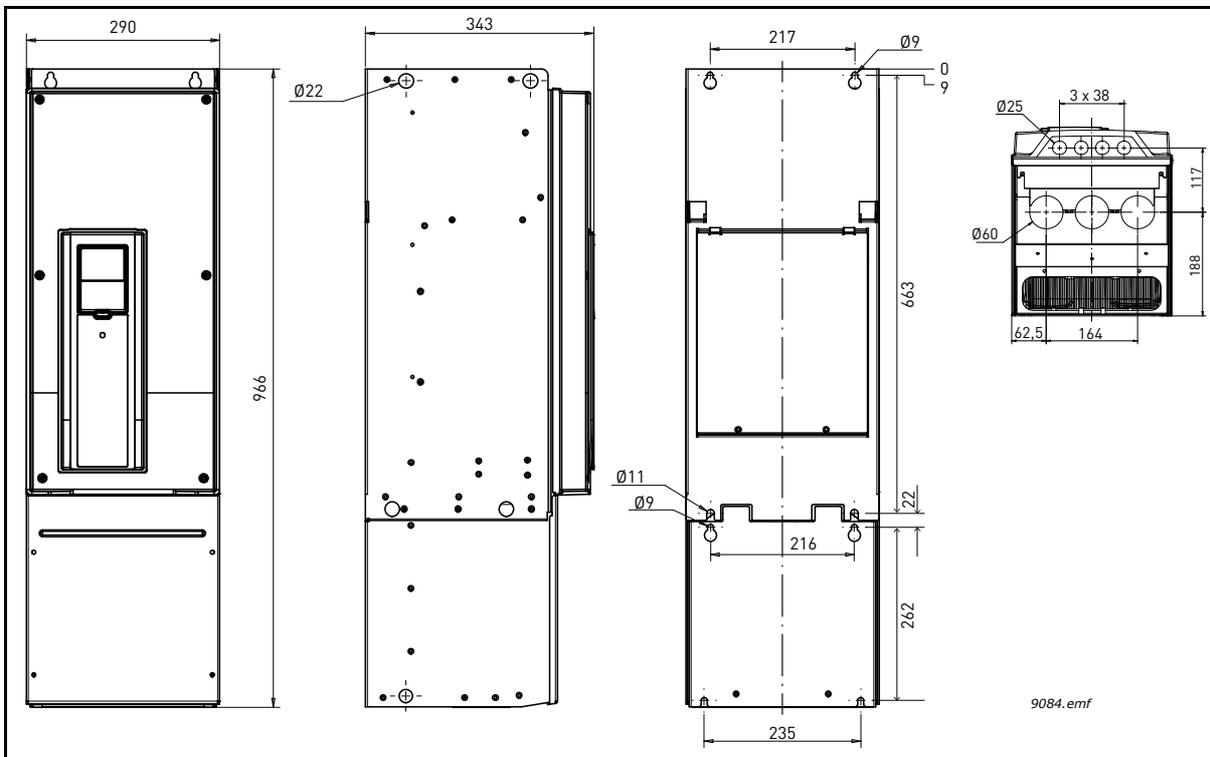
Dimensions SmartDrive, MR8 IP21 et IP54
